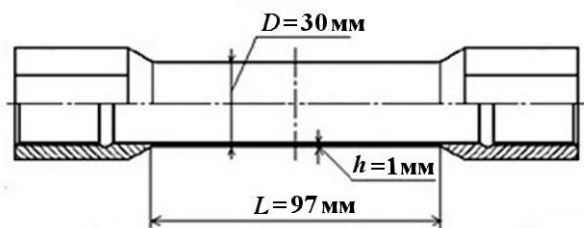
Форма и основные размеры образца из стали 09Г2С
